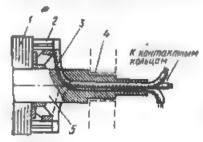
Соединение выводов фаз обмотки с контактными кольцами:
